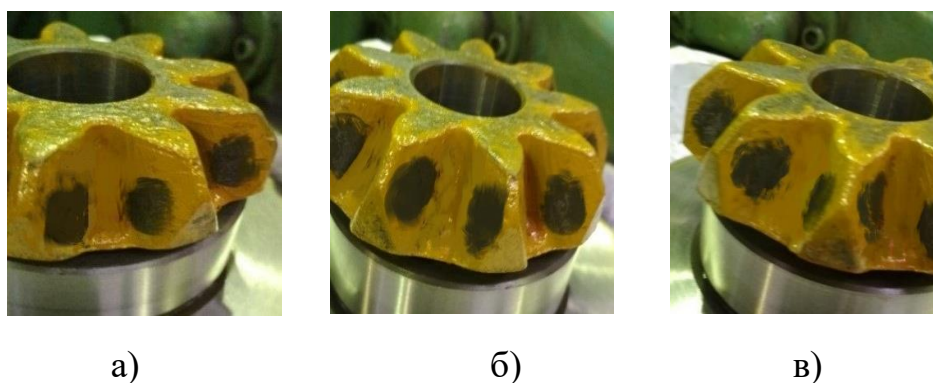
Опытные образцы после калибровочной операции с автоматизированной регулировкой закрытой высоты штампа
